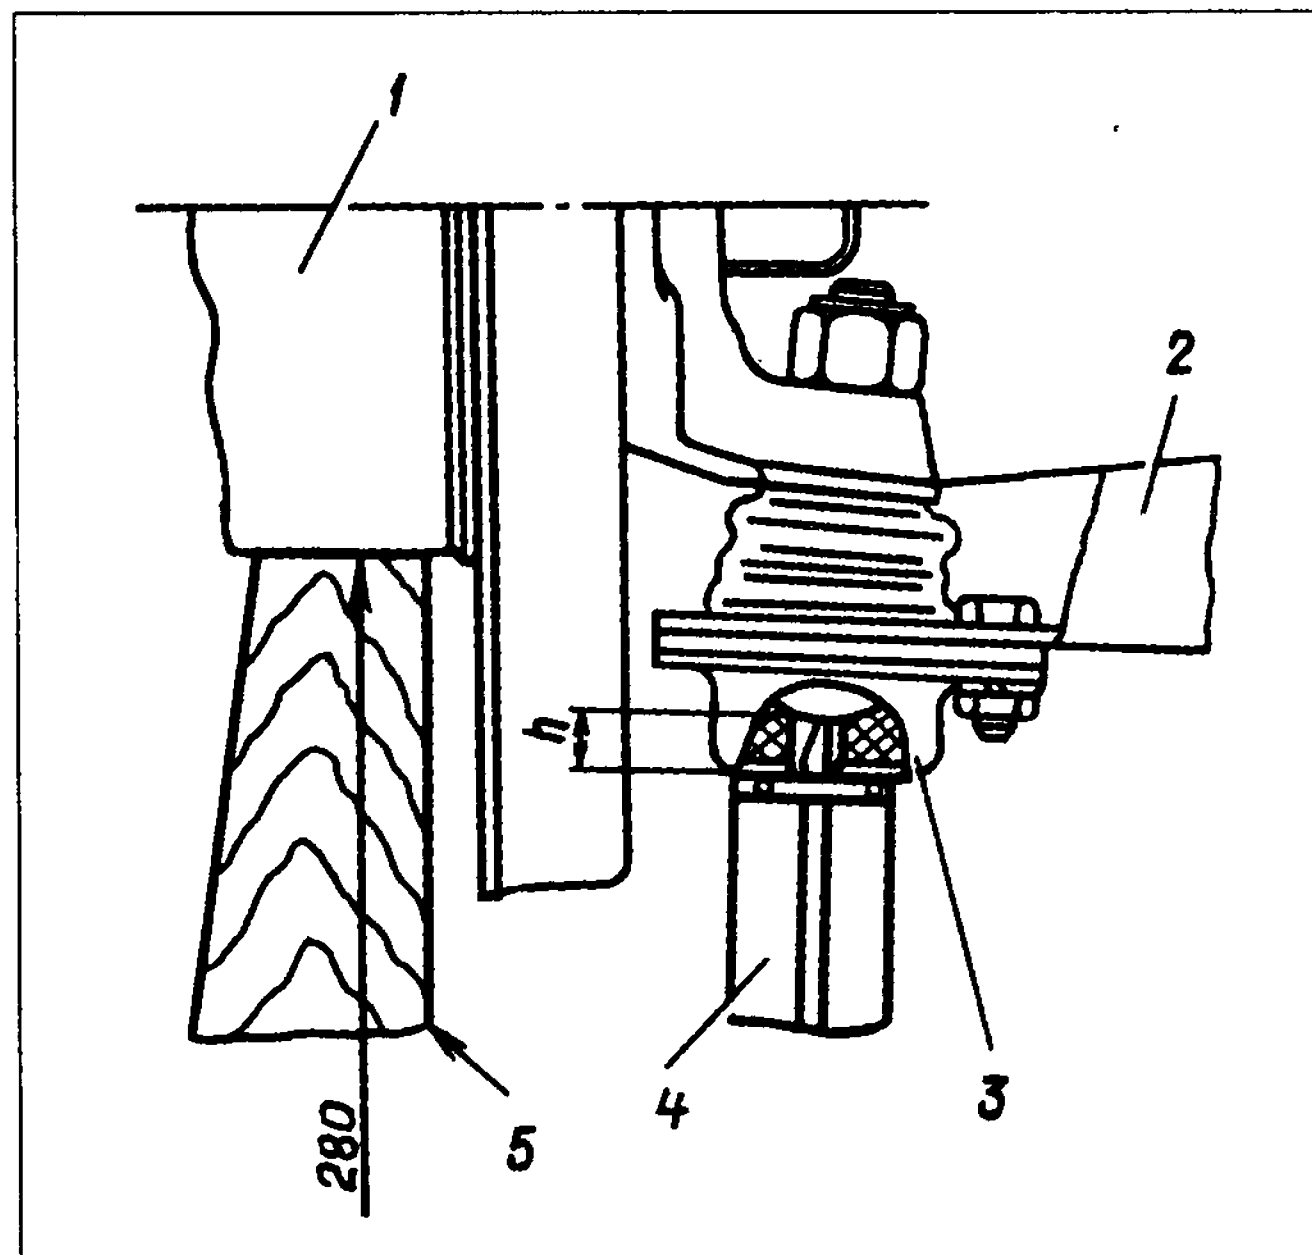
Схема проверки нижних шаровых шарниров: 1-ступица колеса; 2-нижний рычаг; 3-нижний шаровой шарнир; 4-штангенциркуль; 5-деревянная колодка
